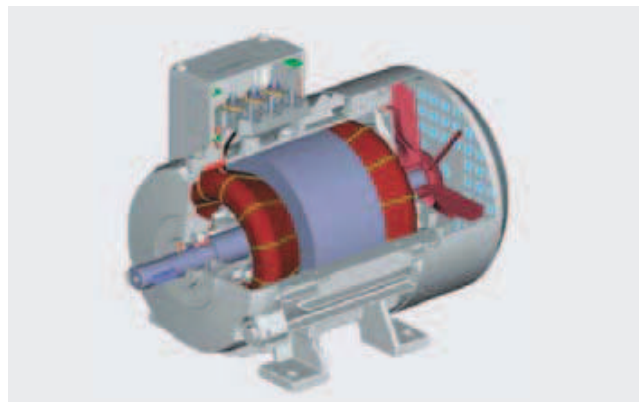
CORTE DE UN MOTOR TRIFASICO
